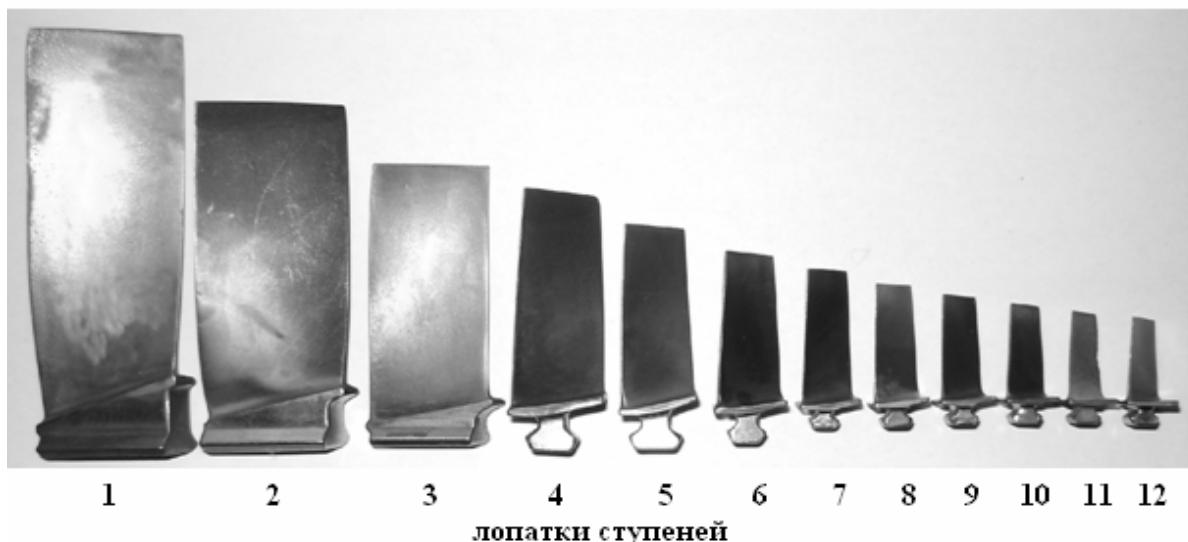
Общий вид лопаток компрессора ГТД модели ТВ3-117
